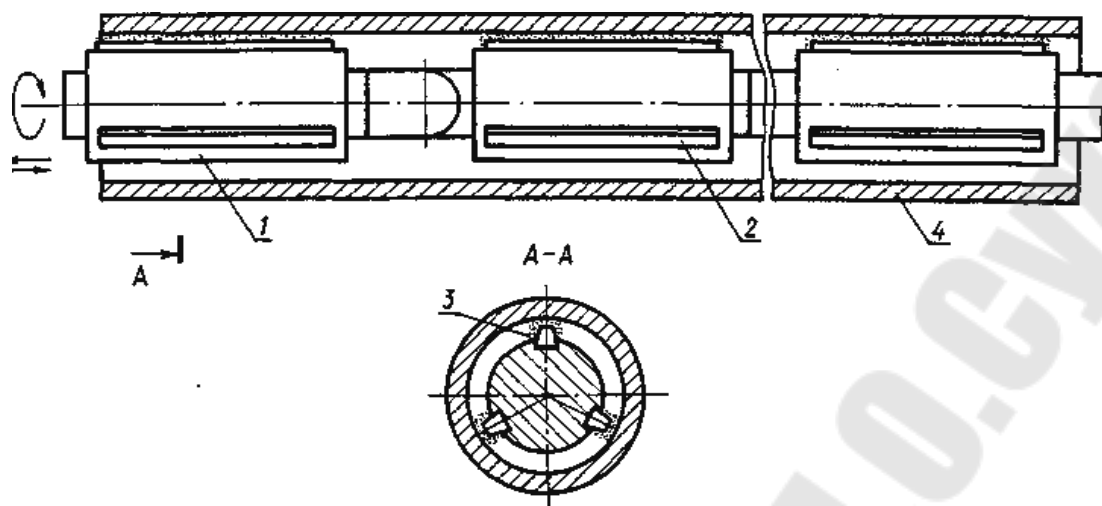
Конструкция индуктора на постоянных магнитах с их параллельным расположением: 1 – каркас из немагнитного материала; 2 – постоянные магниты; 3 – ферроабразивный порошок; 4 – обрабатываемая деталь
